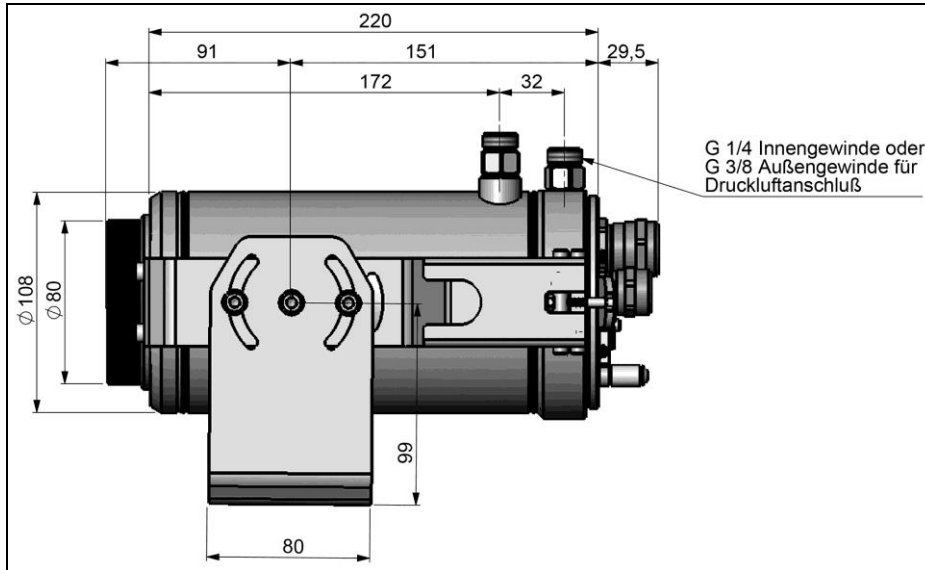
Cooling Jacket Advanced - Seitenansicht
